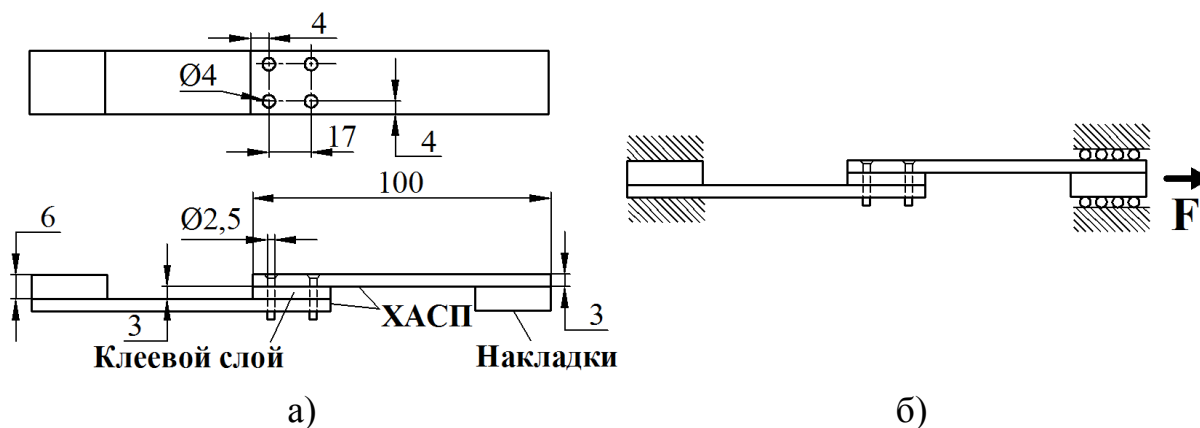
Эскиз образца клеемеханического соединения (а) и схема его нагружения (б)
